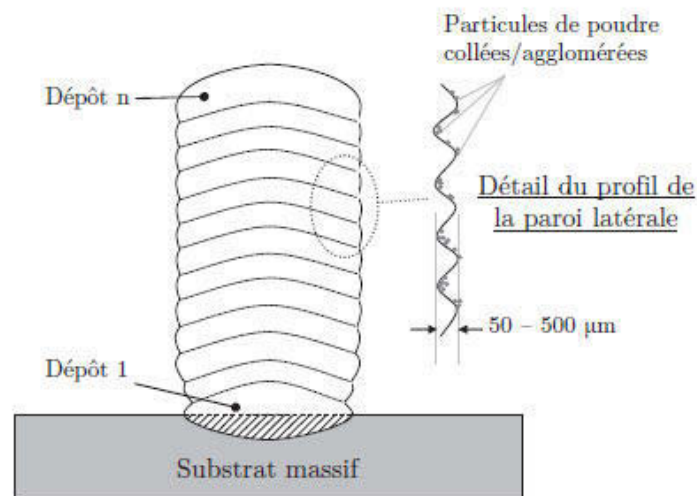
Schéma en coupe transversale d'un mur mince [7]
